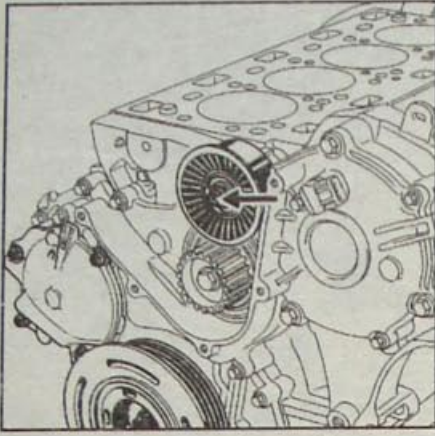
Расположение гайки крепления обводного ролика ремня привода газораспределительного механизма
